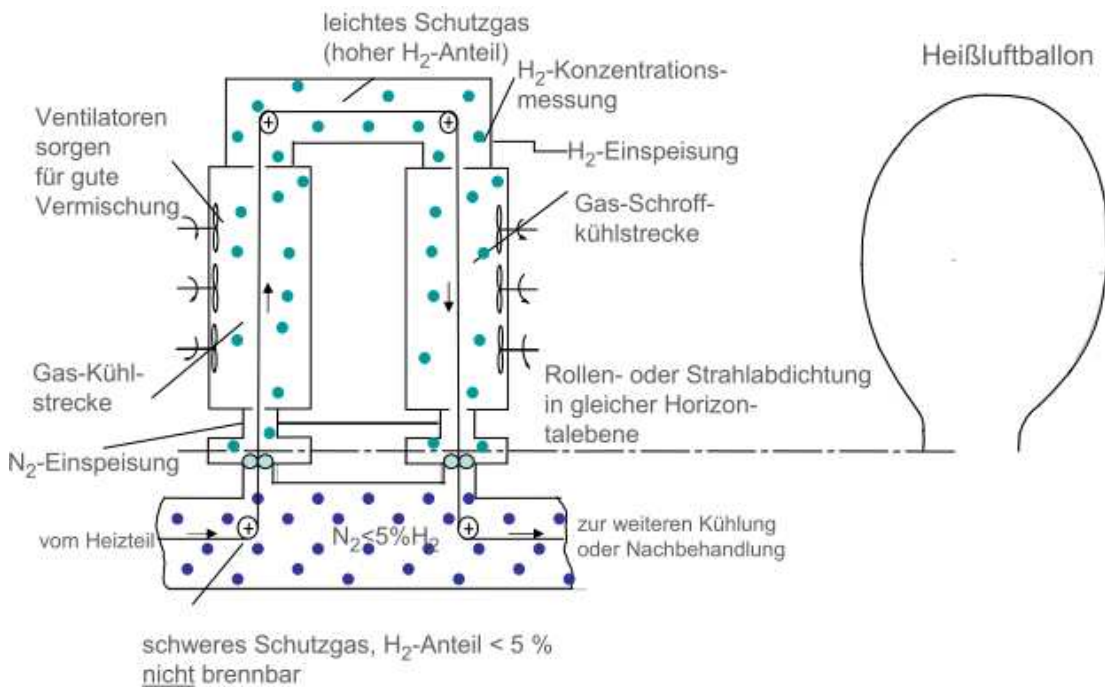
Schema einer WSP-Vertikalkühlstrecke zur Schnellkühlung moderner Stahllegierungen unter Schutzgas mit 85% H₂
